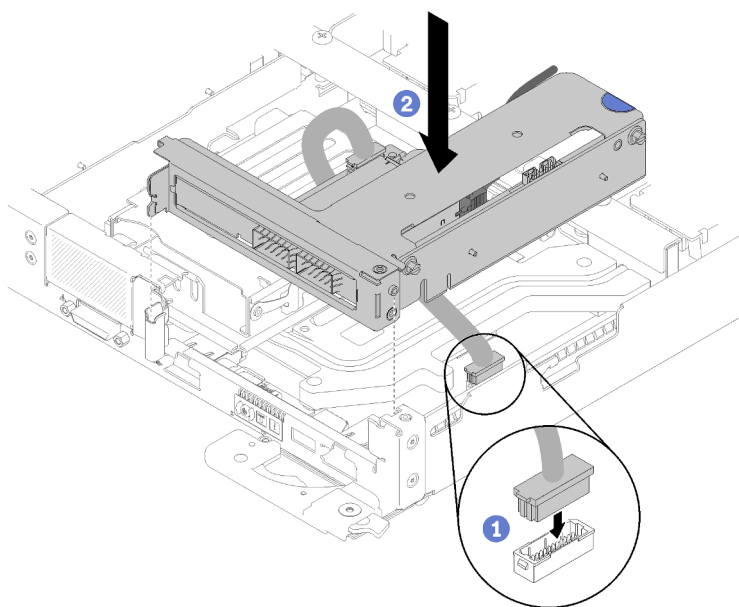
Installation der Gehäusebaugruppe für PCIe-Adapterkarte
